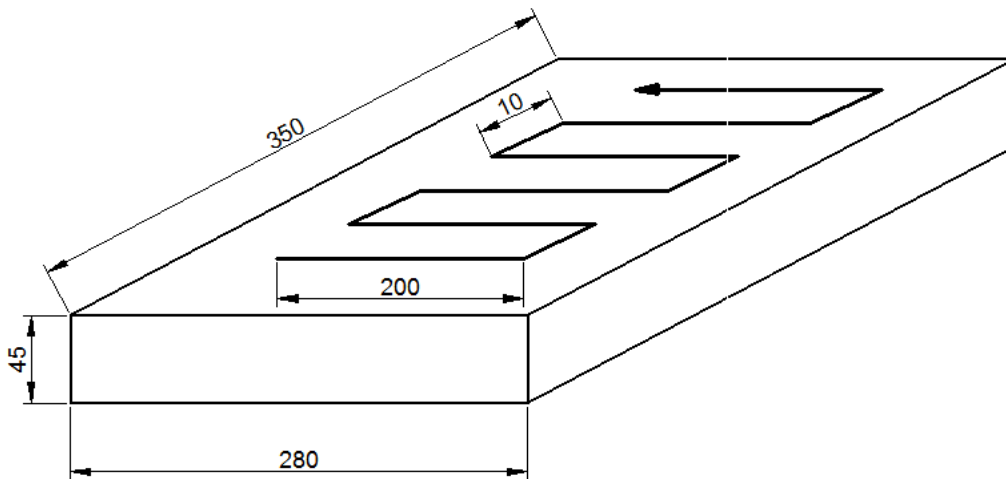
Схема наплавки порошковой лентой с колебаниями порошковой лентой ПЛ-АН101
